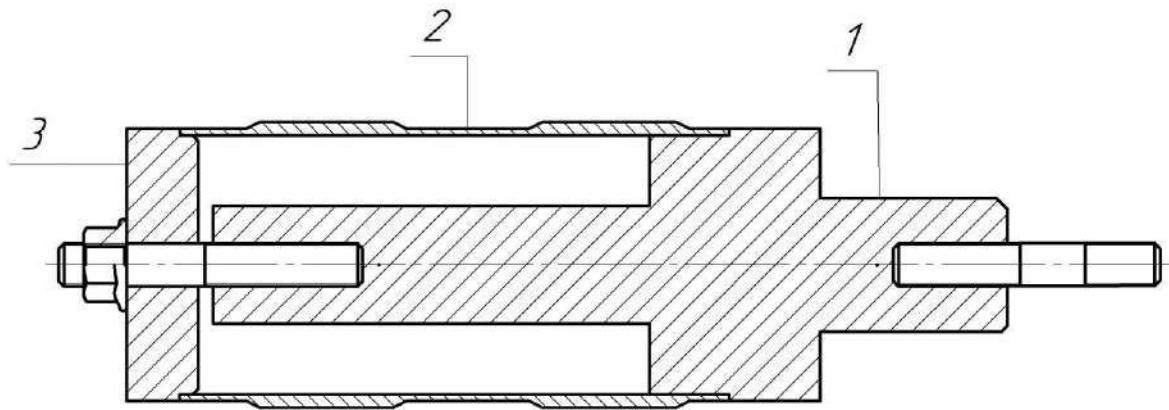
Схема установки втулки на жесткой фрезерной оправке для фрезерования фасонных впадин на цилиндрических утолщениях втулки:
